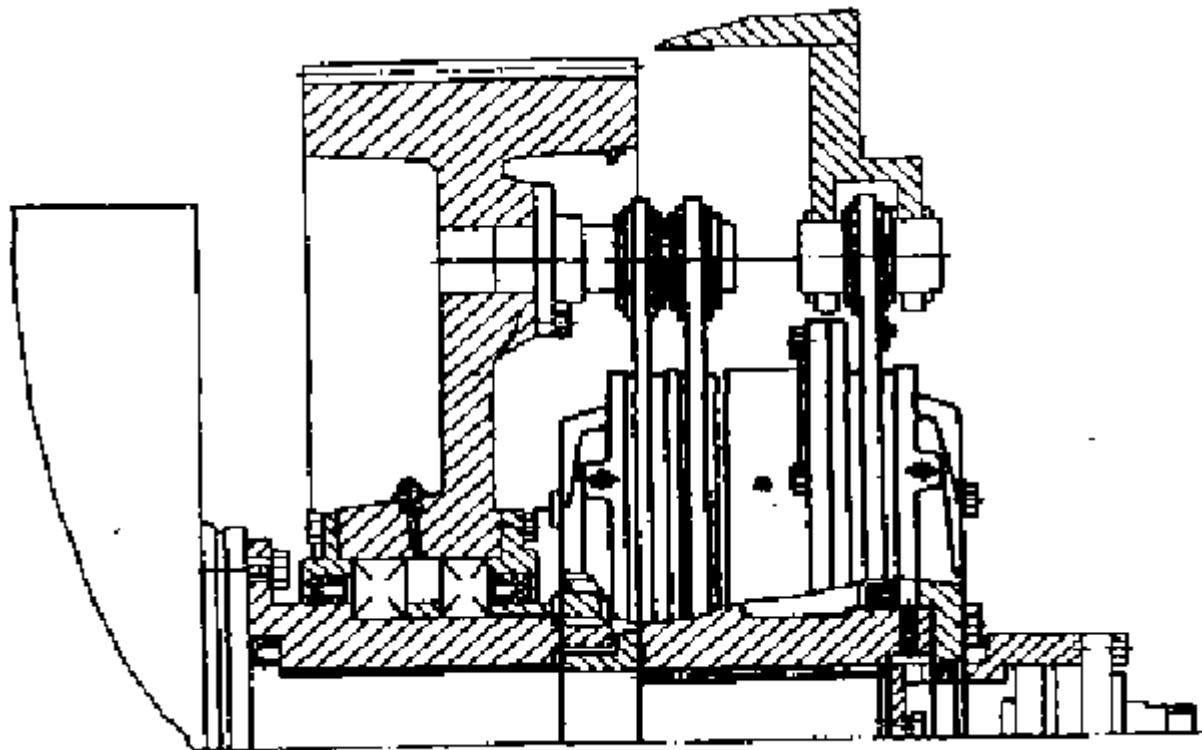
Установка муфты-тормоза на валу, разгруженном от зубчатого колеса, с соединением тормозного диска со станиной через кронштейн и маховик
